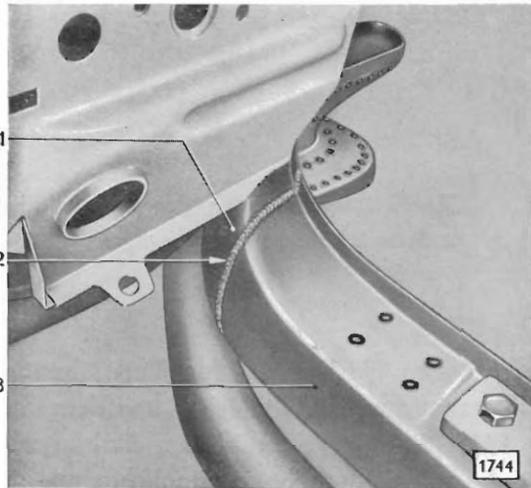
Neuen linken Längsträger entlang der Schnittkante des Längsträgerrestes lichtbogenschweißt – am rechten Längsträger in gleicher Weise lichtbogenschweißen
